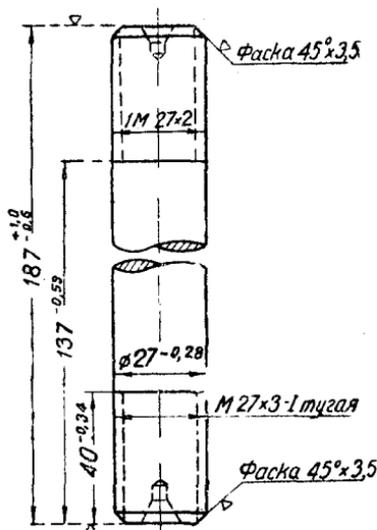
Дет. А02-11. Шпилька коренного подшипника
